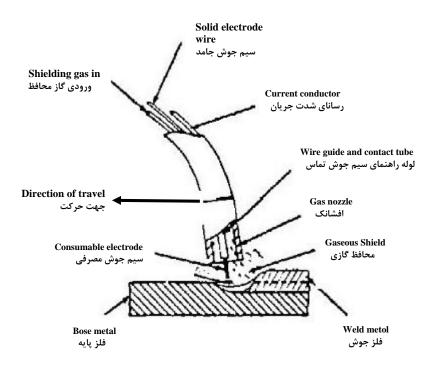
GAS METAL ARC WELDING PROCESS شکل Λ فر آیند جوشکاری قوسی با میل جوش فلزی تحت گاز محافظ
